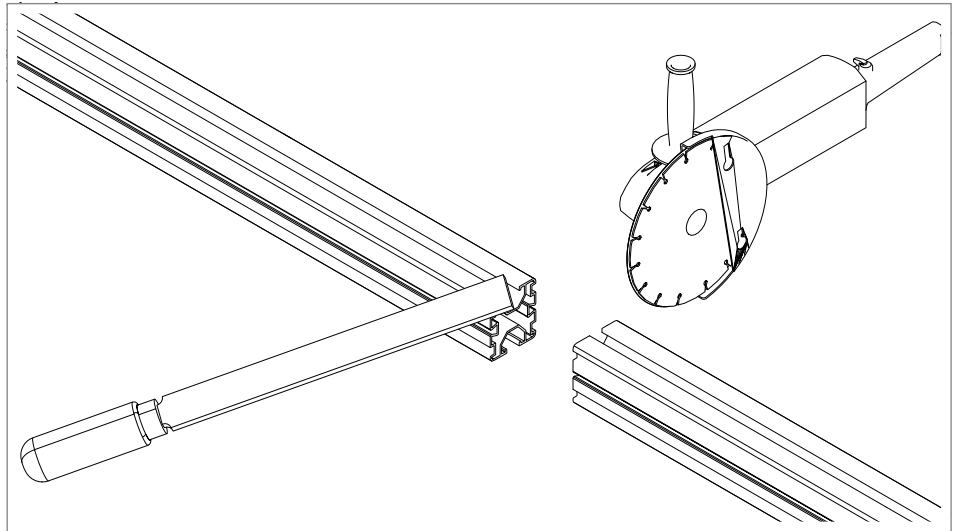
Cortar o perfil de estrutura no comprimento desejado
